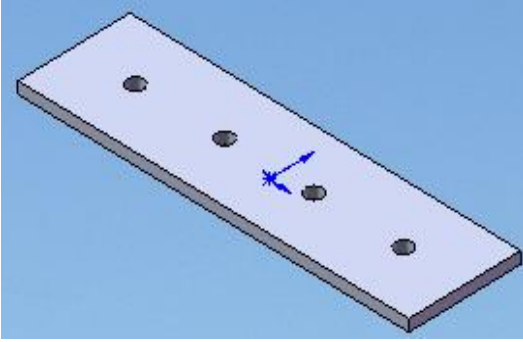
Vakum Kalıbı Montaj Gösterimi
